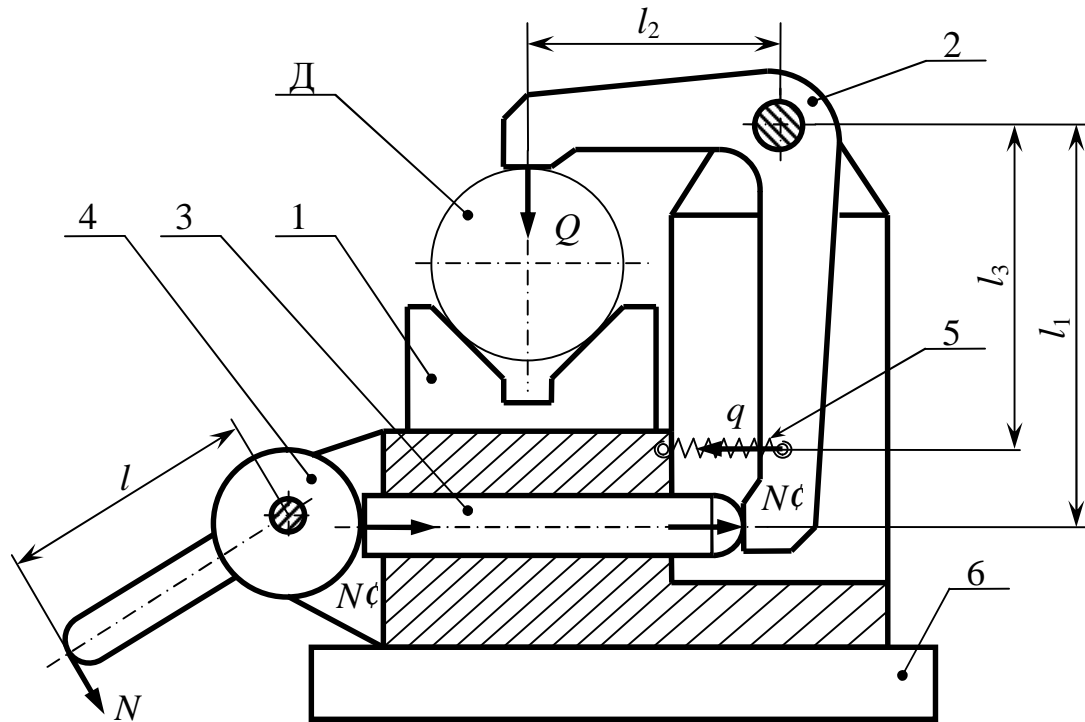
Компоновка станочного приспособления: Д – заготовка, 1 – установочный элемент (призма); 2 – зажимной элемент (рычаг); 3 – толкатель; 4 – круглый эксцентрик; 5 – возвратная пружина; 6 – корпус приспособления; N – исходная сила, приложенная к рукоятке эксцентрика; $N\zeta$ – сила, вырабатываемая эксцентриком (передается толкателем на рычаг); Q – требуемая сила закрепления; q – сила растяжения пружины; l – длина рукоятки эксцентрика; l_1 и l_2 – плечи рычага; l_3 – размер, определяющий место установки возвратной пружины
